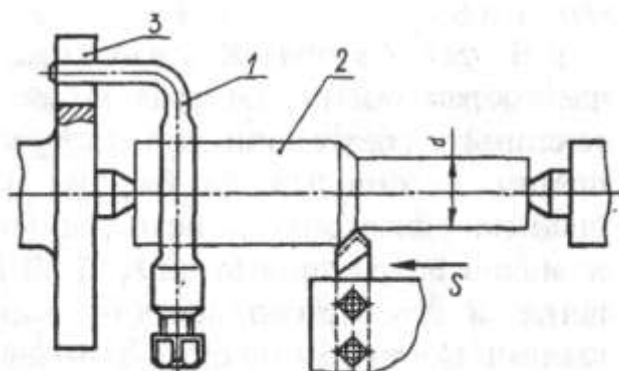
Схема поводкового приспособления для вращения детали при обработке на токарном станке
